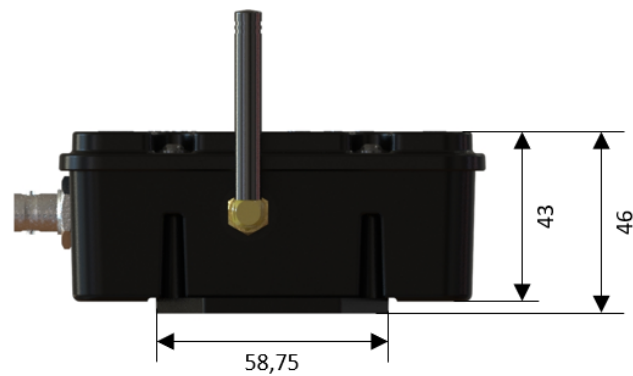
Dimensões [mm] externas do WEGscan400 com presilha para superfícies planas - Vista lateral
